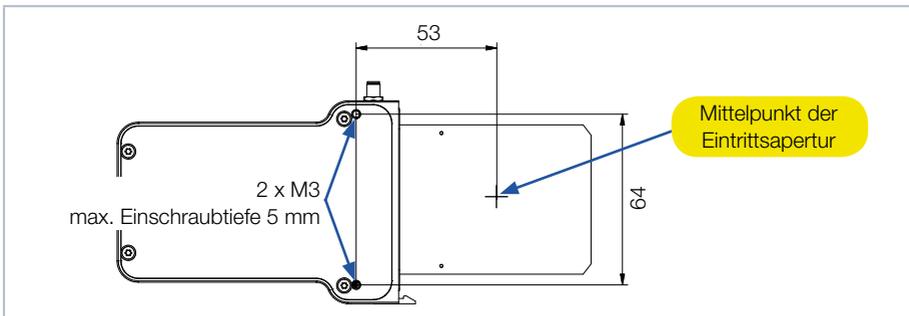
Befestigungsgewinde im Gehäuse (Maße in mm)
